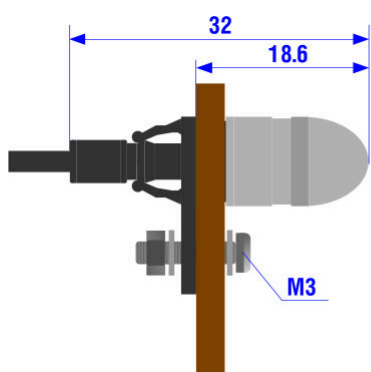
Установочные размеры для крепления ВОД с внешней стороны ячейки, мм
